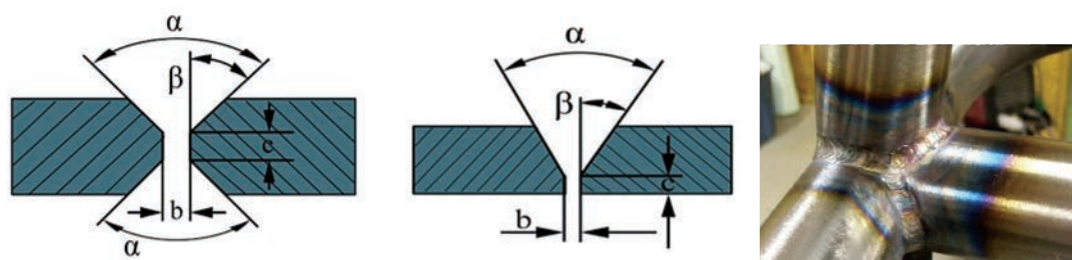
Схеми розділок під зварювання з обробленими перлітними крайками:
